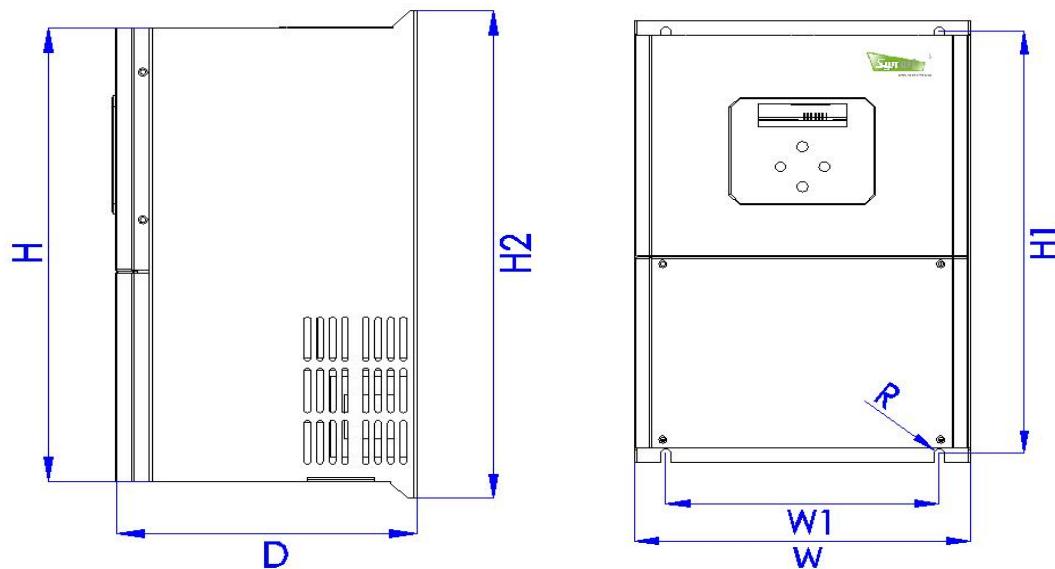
SM10 系列 11~160kW 安装及外形尺寸示意图
